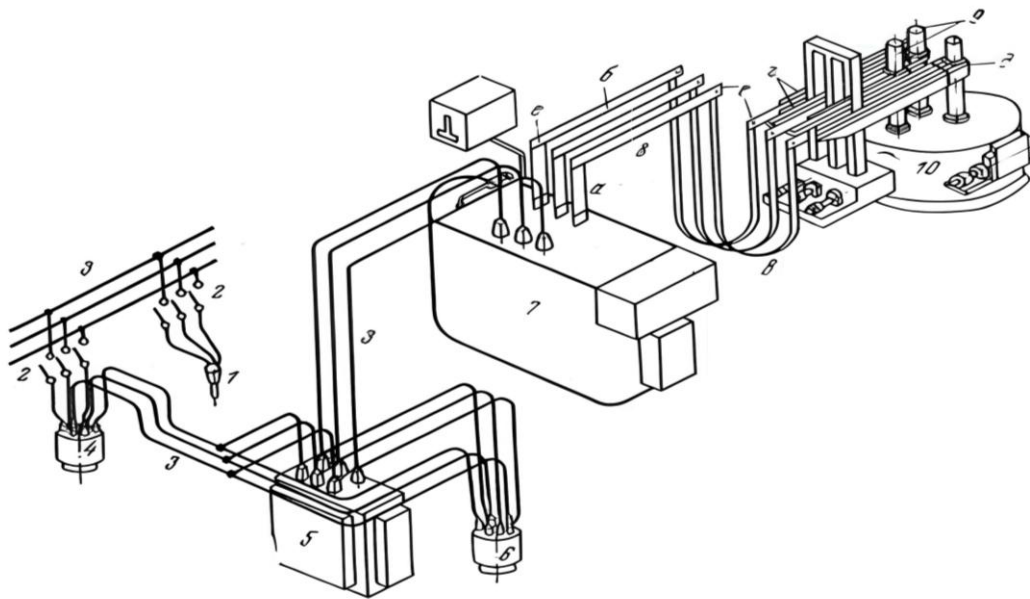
Схема конструкції дугової сталеплавильної печі
